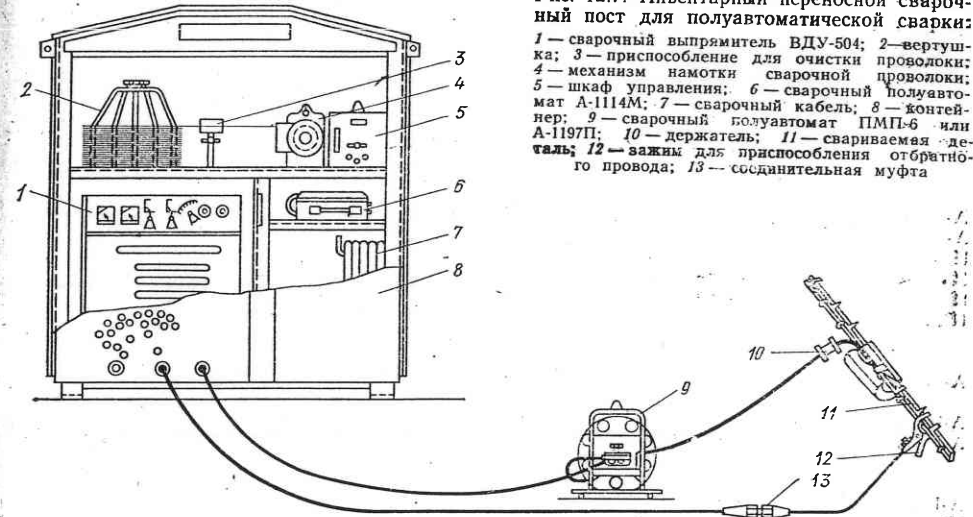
Инвентарный переносной сварочный пост для полуавтоматической сварки: 1 — сварочный выпрямитель ВДУ-504; 2 — вертушка; 3 — приспособление для очистки проволоки; 4 — механизм намотки сварочной проволоки; 5 — шкаф управления; 6 — сварочный полуавтомат А-1114М; 7 — сварочный кабель; 8 — контейнер; 9 — сварочный полуавтомат ПМП-6 или А-1197П; 10 — держатель; 11 — свариваемая деталь; 12 — зажим для приспособления обратного провода; 13 — соединительная муфта
